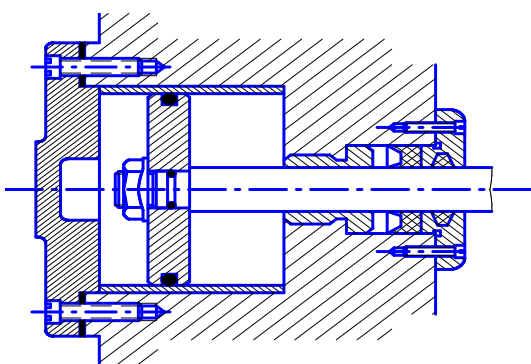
Типовая компоновка встроенного пневмоцилиндра
